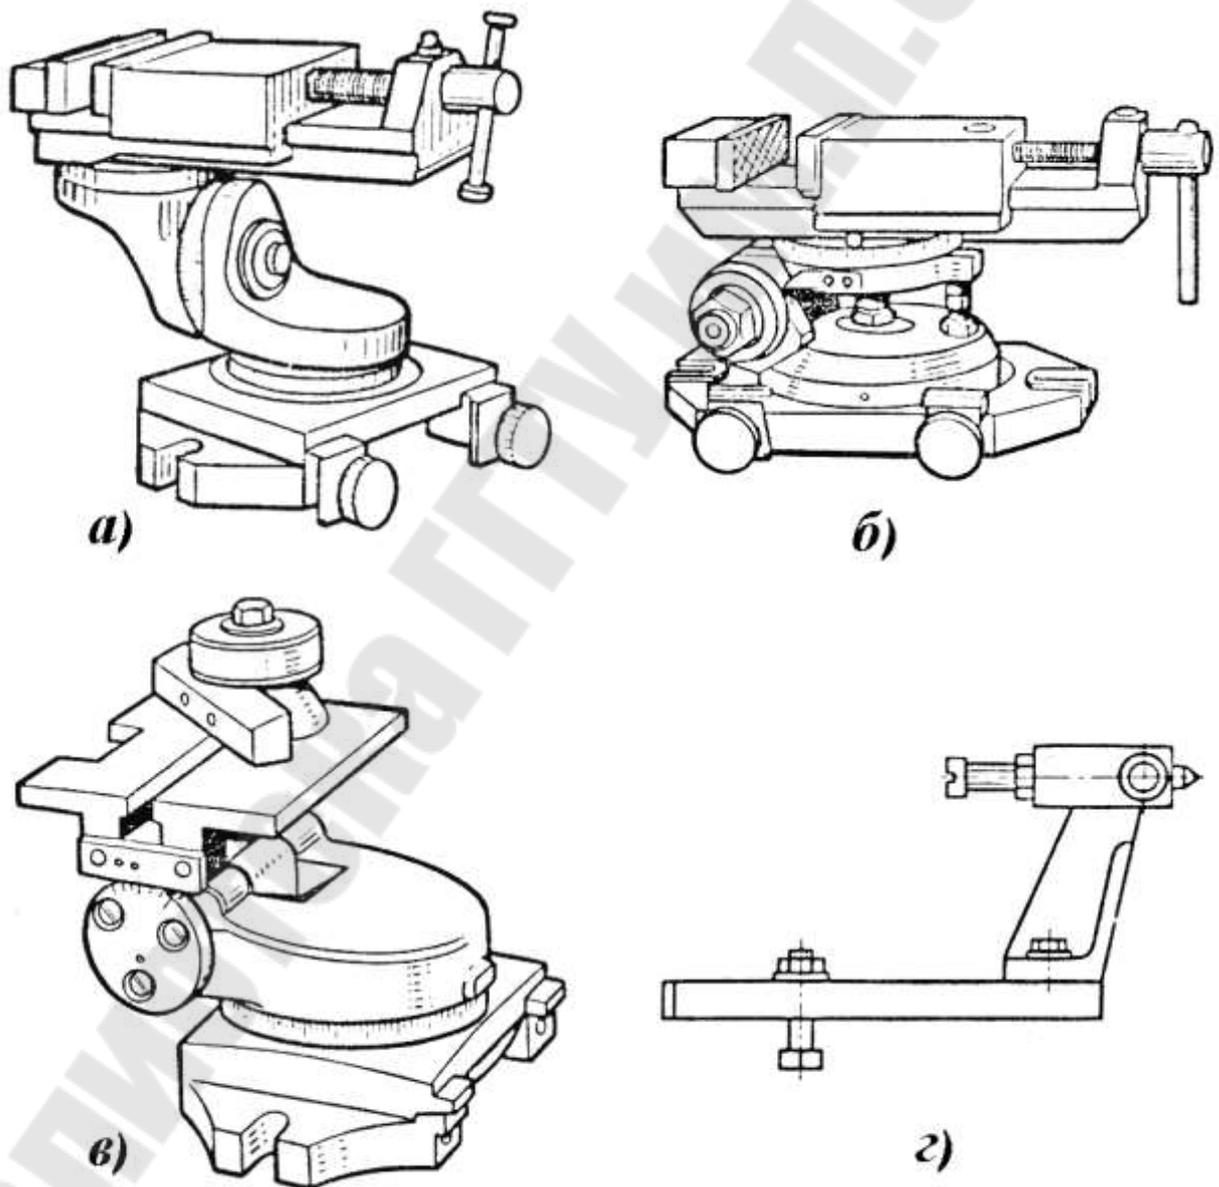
Универсальные тиски (а); наклонно-поворотные тиски (б); подручник (в); приспособление для линейной правки круга(г).
